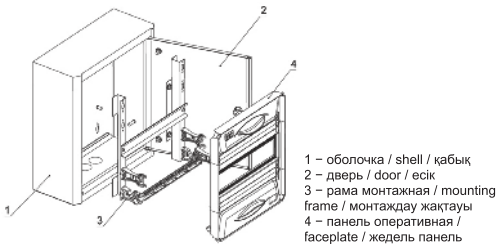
Состав корпуса / Figure 1 – Enclosure component parts / 1 сурет – Корпусстың құрамы
